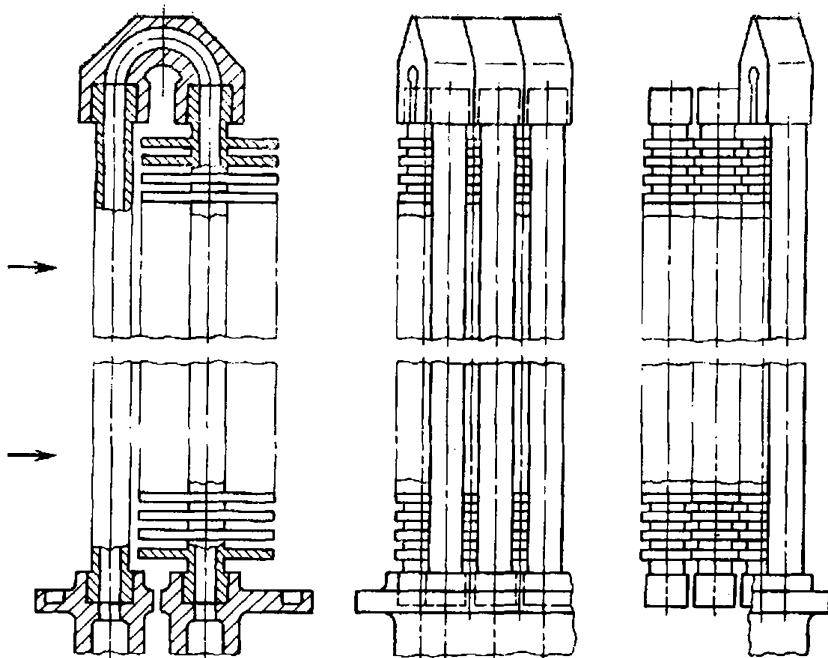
Элементы нагревательных труб четырехцилиндрового двигателя Стирлинга двойного действия [4]
